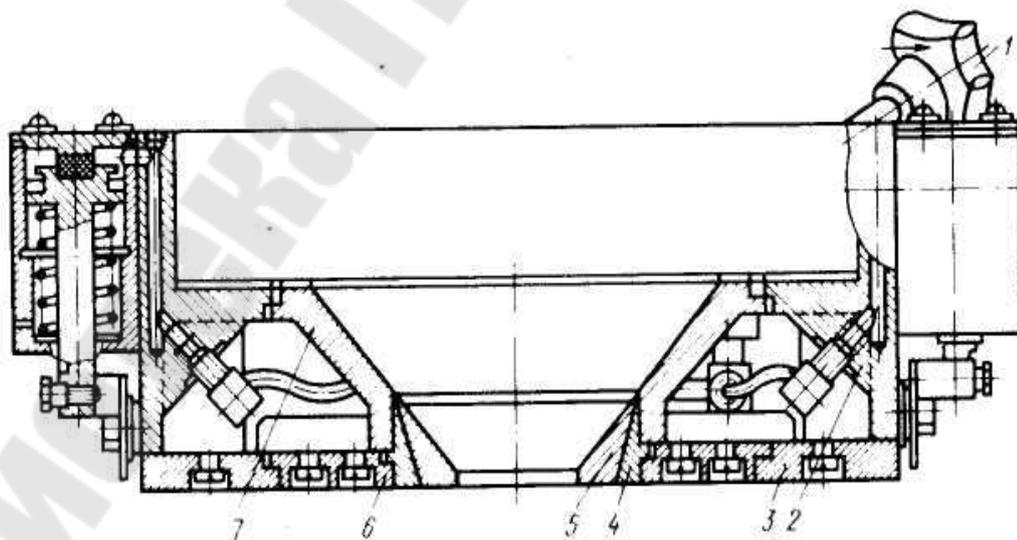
Устройство насадки пескоструйного резервуара полуавтомата мод.2Б83
